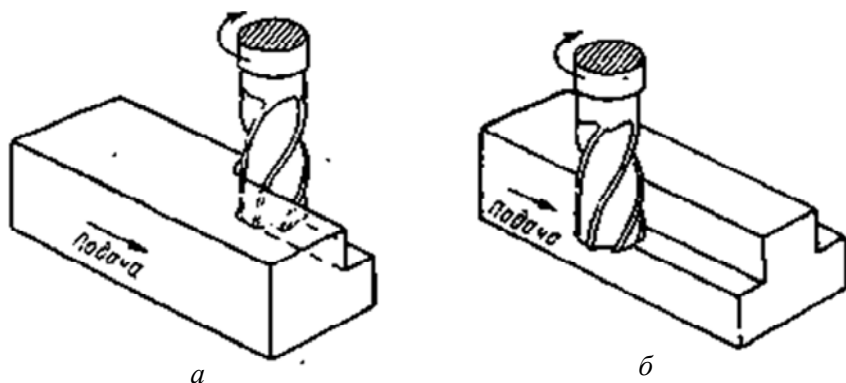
Фрезерование 2-х уступов концевой фрезой: *а* – правого; *б* – левого
